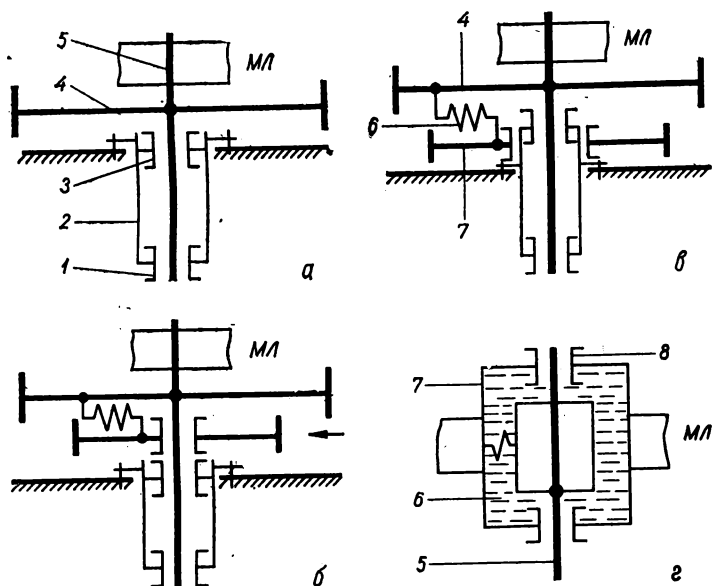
Кинематические схемы узлов ведущего вала исполнения III.
